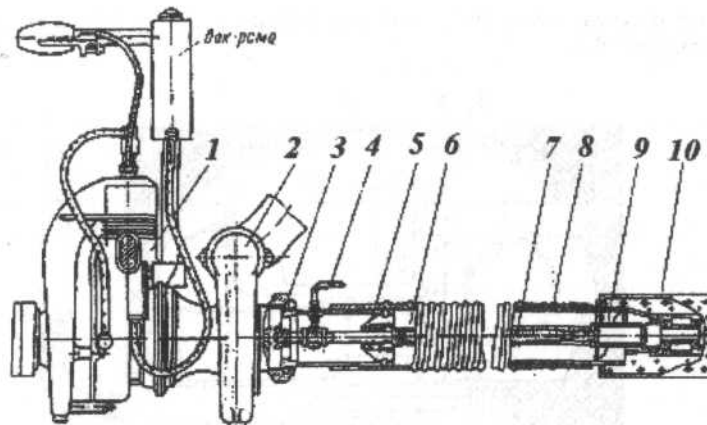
Малогабаритная мотопомпа МЛН-2,5/0,25: 1 - двигатель; 2 - центробежный насос; 3 — полумуфта; 4 - ручка-переключатель; 5 - направляющая втулка; 6 - хвостовик; 7 - гибкий вал; 8 — всасывающий рукав; 9 - осевой насос; 10 — сетчатый фильтр
